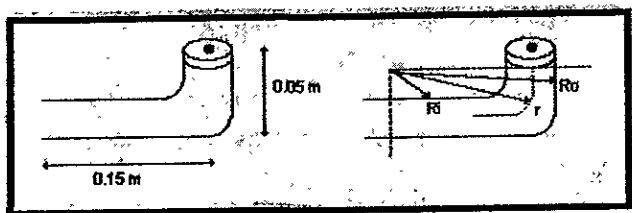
DIMENSIONES DEL CODO DE TUBO
